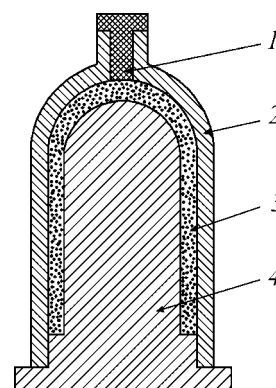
Схема пресс-формы для получения изделий в виде трубок: 1 — пробка, закрывающая отверстие для засыпки порошка; 2 — эластичная оболочка; 3 — порошок; 4 — стальной стержень.
